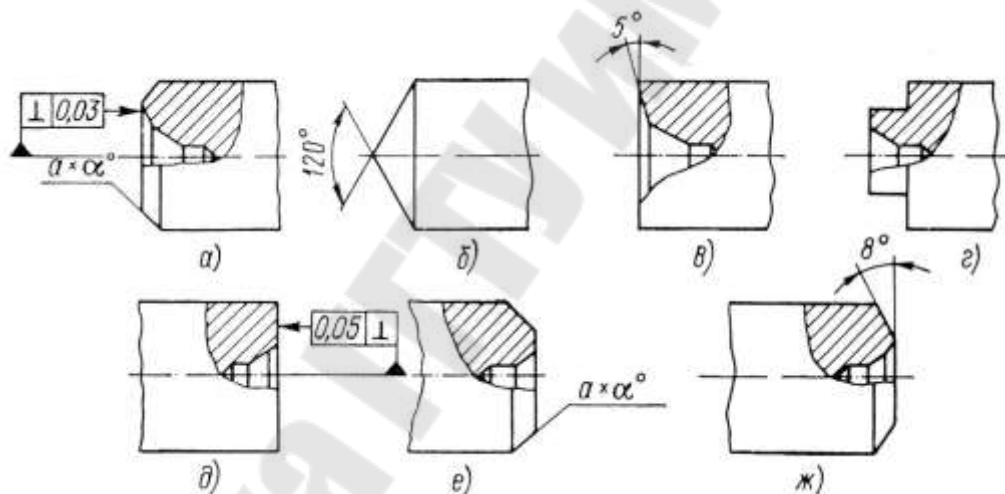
Эскизы торцов заготовок концевых инструментов
